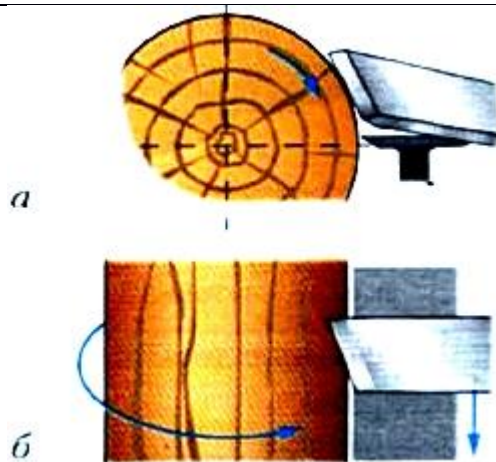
Чистовое точение косой стамеской: а — вид с торца заготовки; б — вид сверху
